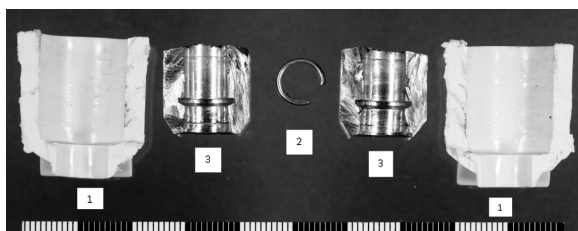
Корпус стержневого пломбировочного устройства «С-1-0504» после его разборки
